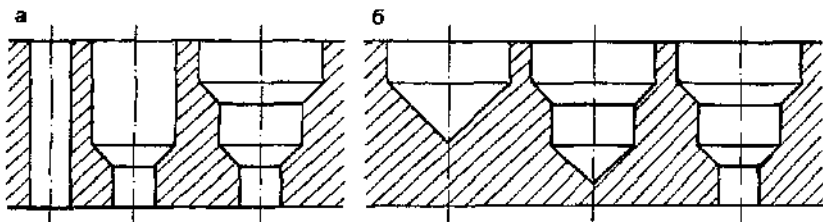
Сверление отверстий с уступами: а — рассверливанием; б — с уменьшением диаметра отверстия
